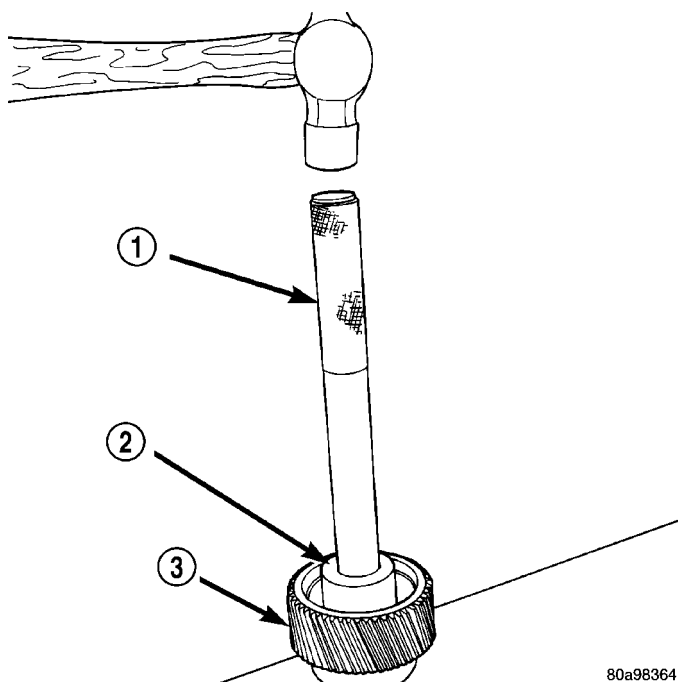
Instalación del cojinete de guía del engranaje impulsor
